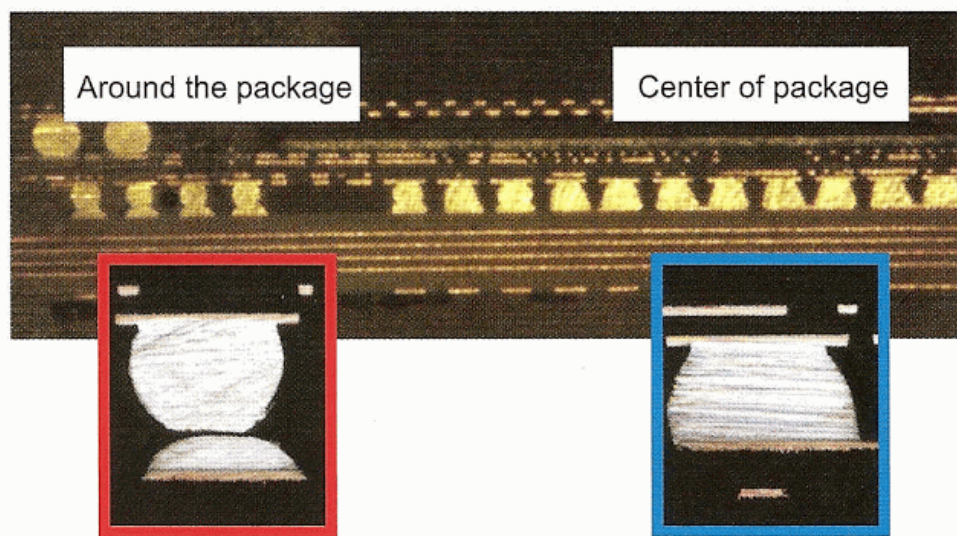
Defekt BGA – black pad efekt (detail) (převzato z [29])
